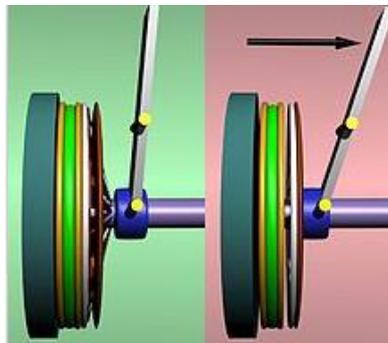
Embrague acoplado (izquierda) y desacoplado (derecha)
